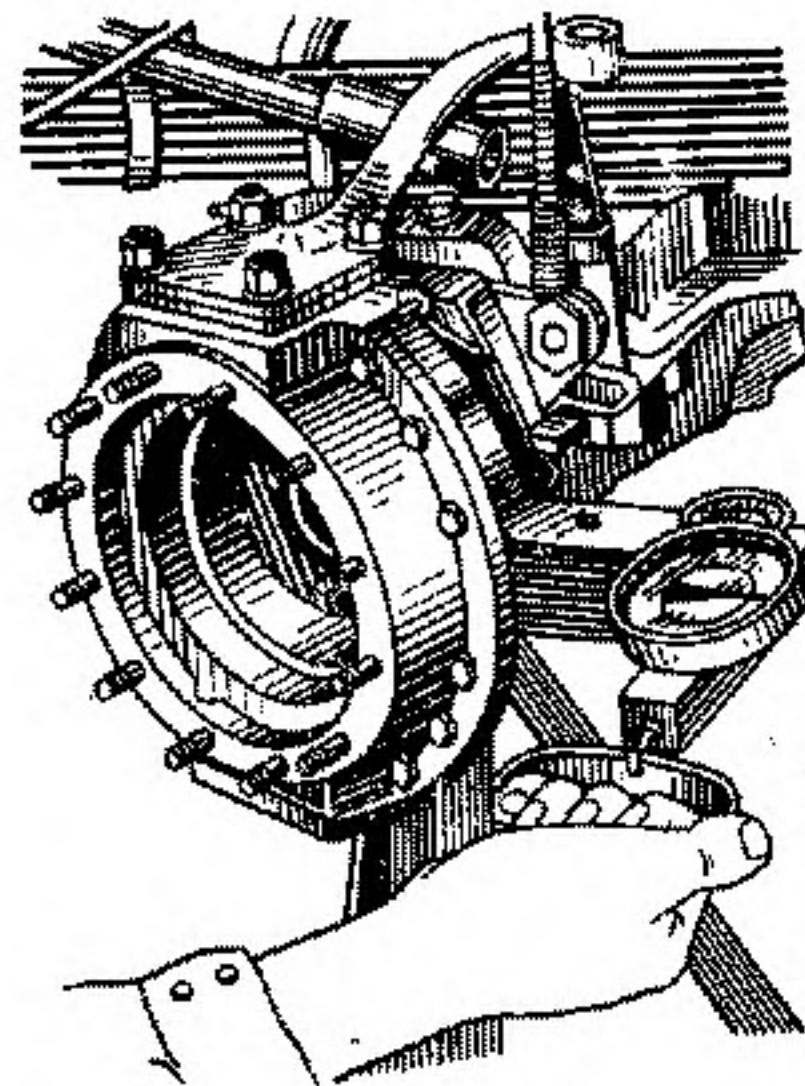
Проверка затяжки подшипников шкворней поворотного кулака автомобиля ГАЗ-66-11 с помощью динамометра
